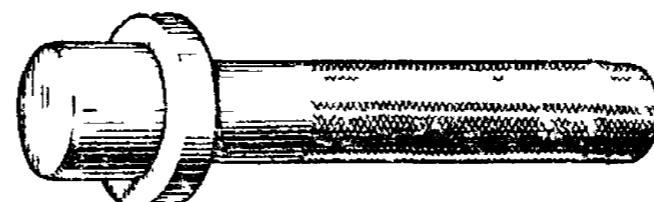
Оправка для демонтажа подшипника из переднего корпуса
